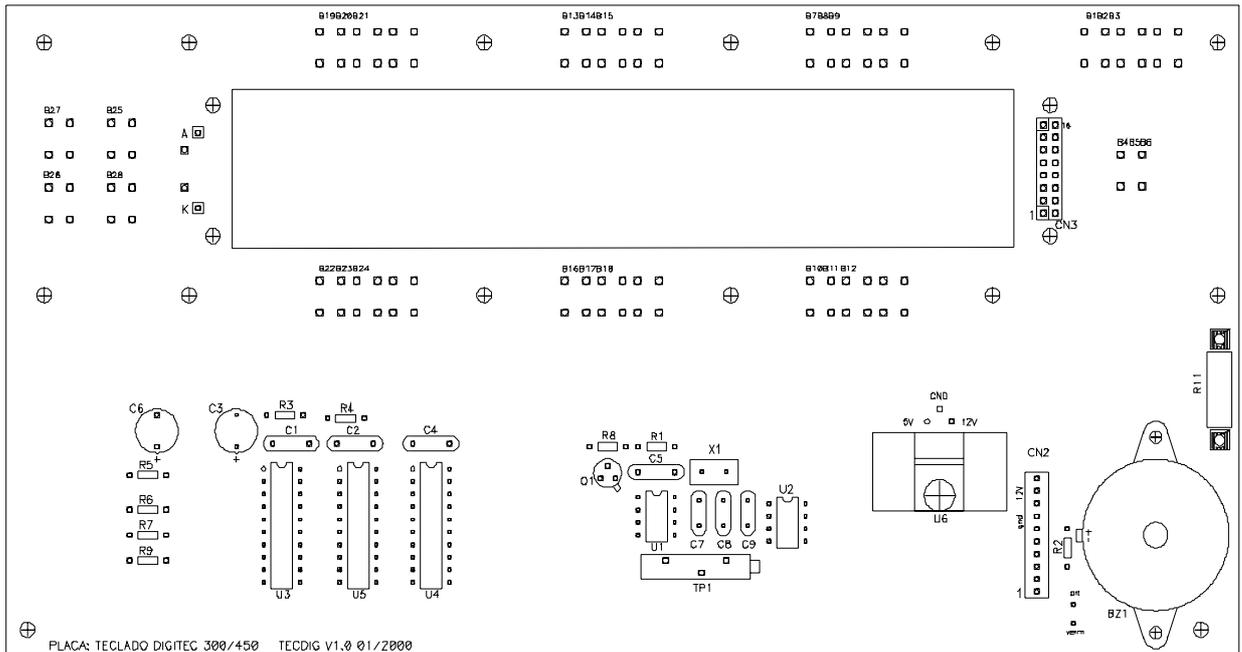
LAYOUT da placa de controle e do teclado do painel.
